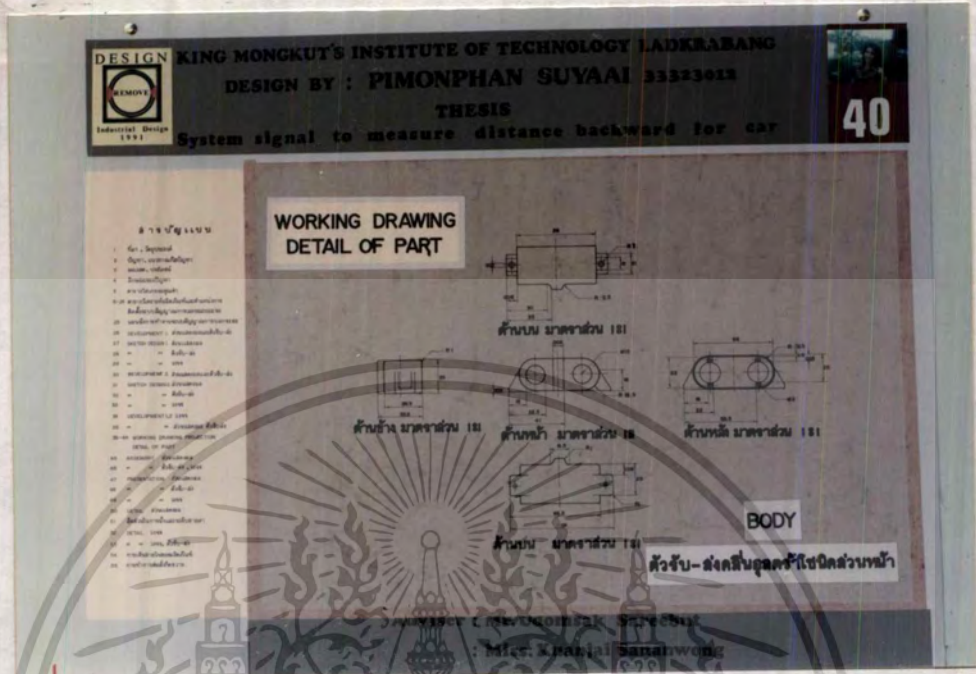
WORKING DRAWING / PROJECTION VIEW
